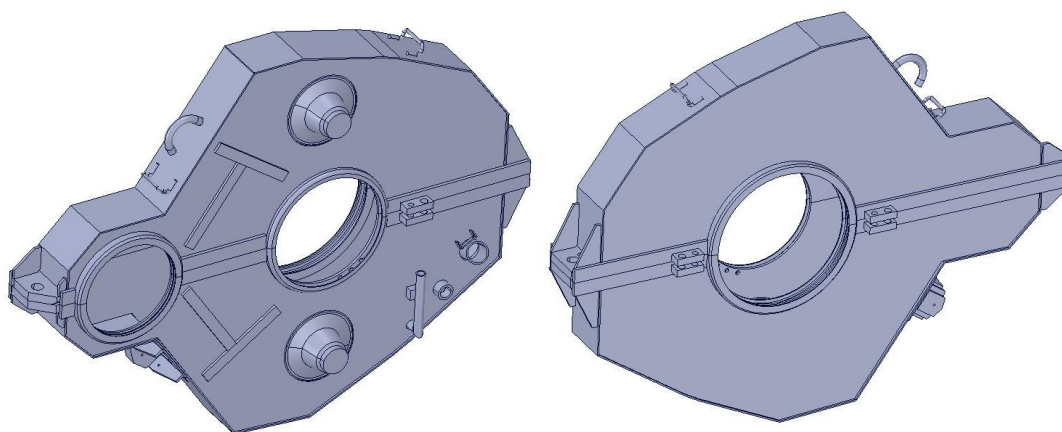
Серийно выпускающийся кожух 5ТС.300.296, изготовленный из прямых стальных листов методом сварки
